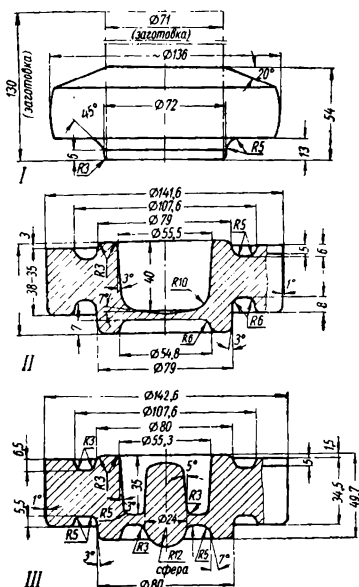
Штамповка шестерни в закрытом штампе в три перехода I—III
